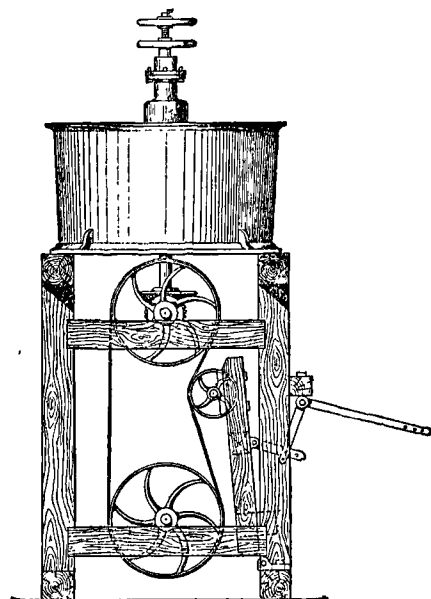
Chaudière de Mac Cone ; vue extérieure.
